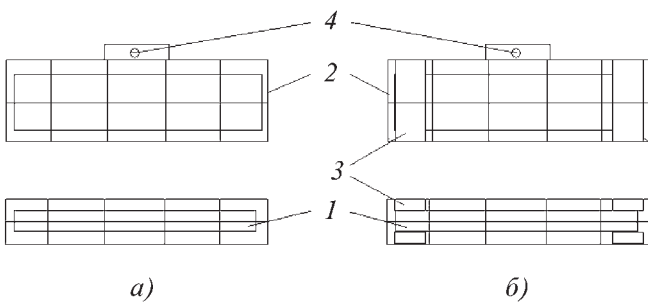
Схемы установки фрагментов лонжерона в решетчатых отсеках приспособления:
